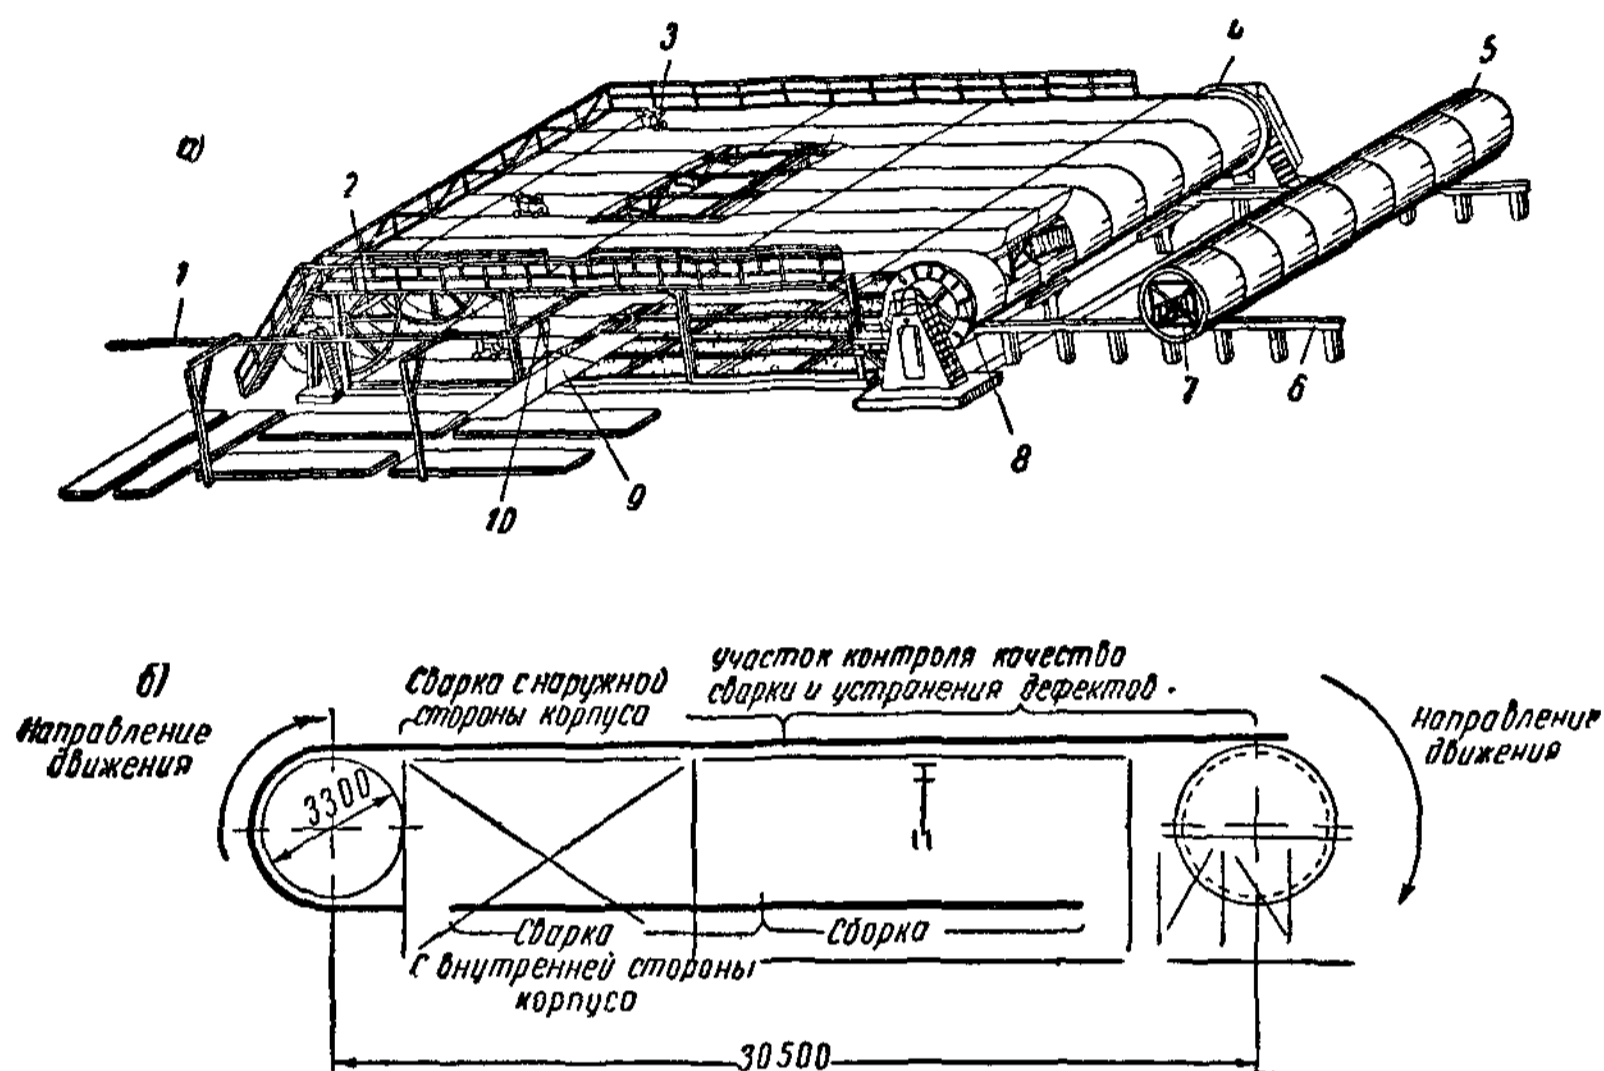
Двухъярусный стенд для изготовления негабаритных цилиндрических резервуаров способом рвлонирования
